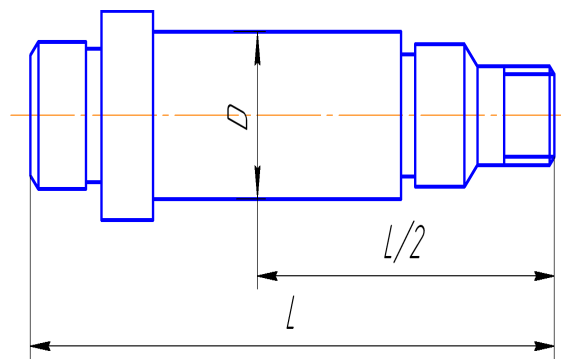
Простановка размеров на чертежах деталей вращения
